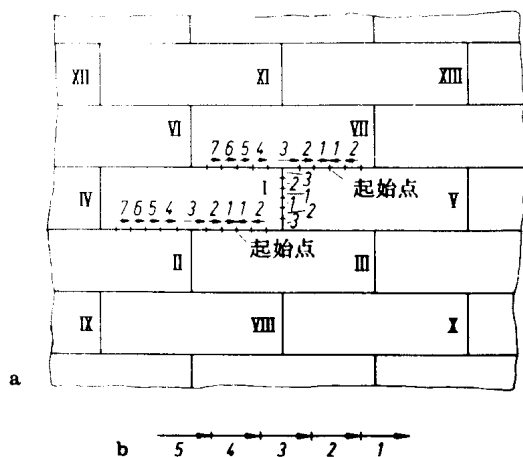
焊接次序。a. 平板壁板的纵向焊缝的焊接步骤排列次序(1至7)和横向焊缝的排列次序I至XIII (焊接顺序1至3); b. 分段退焊法。
